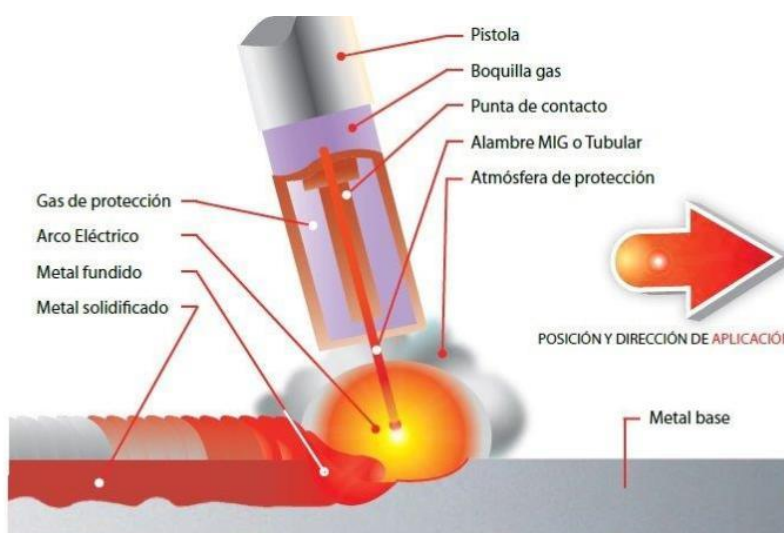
Soldadura por arco con alambre y protección gaseosa
